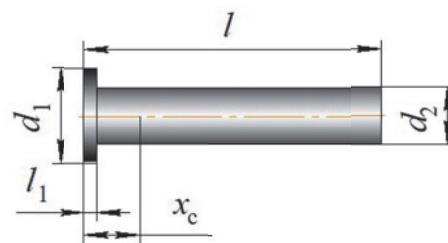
Стержневая заготовка с фланцем и ее основные параметры
